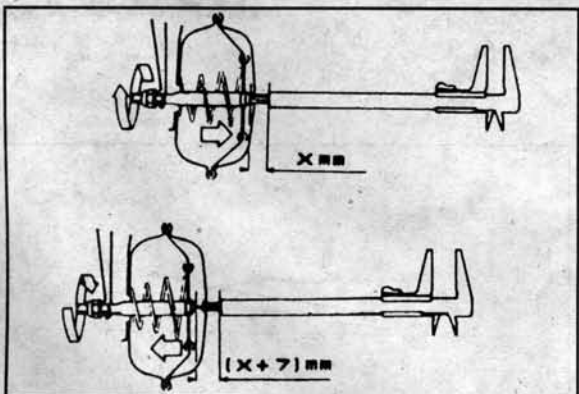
Регулировка сцепления, сопряженного с передачей CVT – установка положения мембраны пневмоцилиндра
